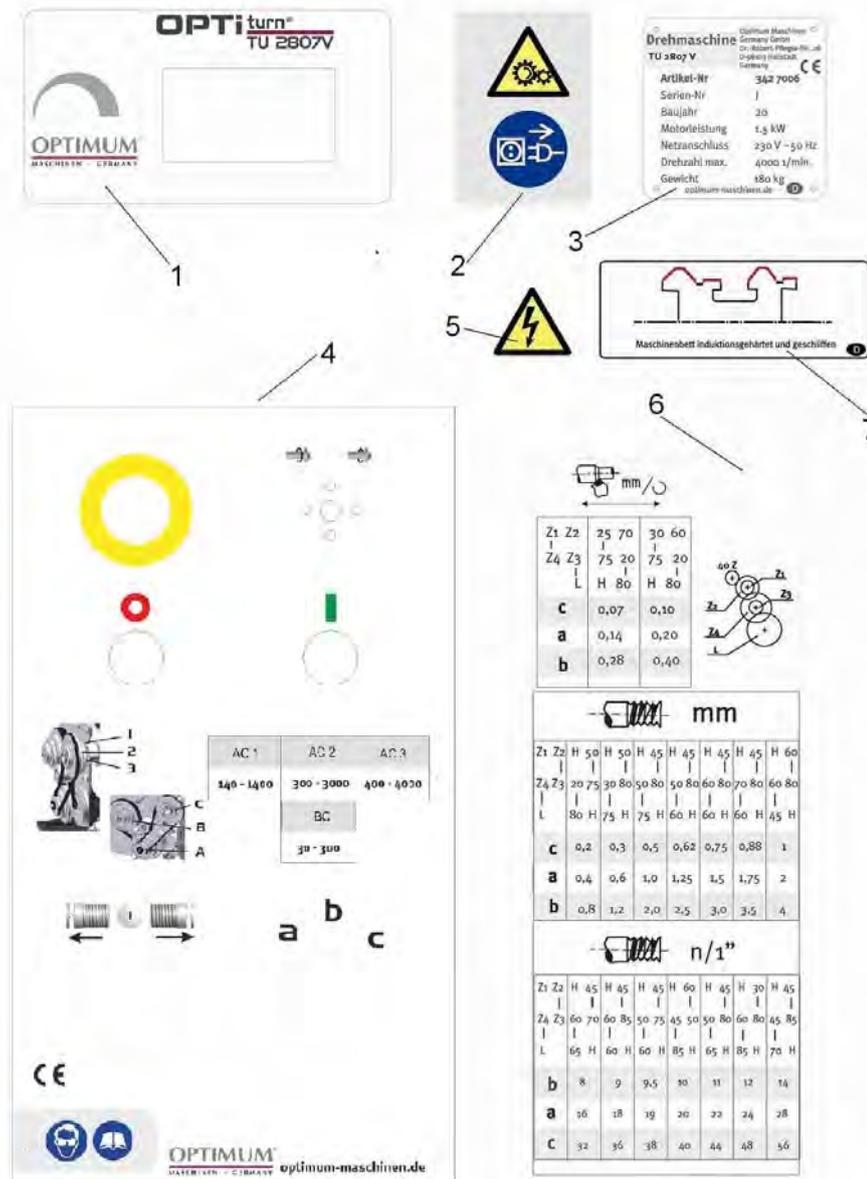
Maschinenschilder - Etiquetas de la máquina
